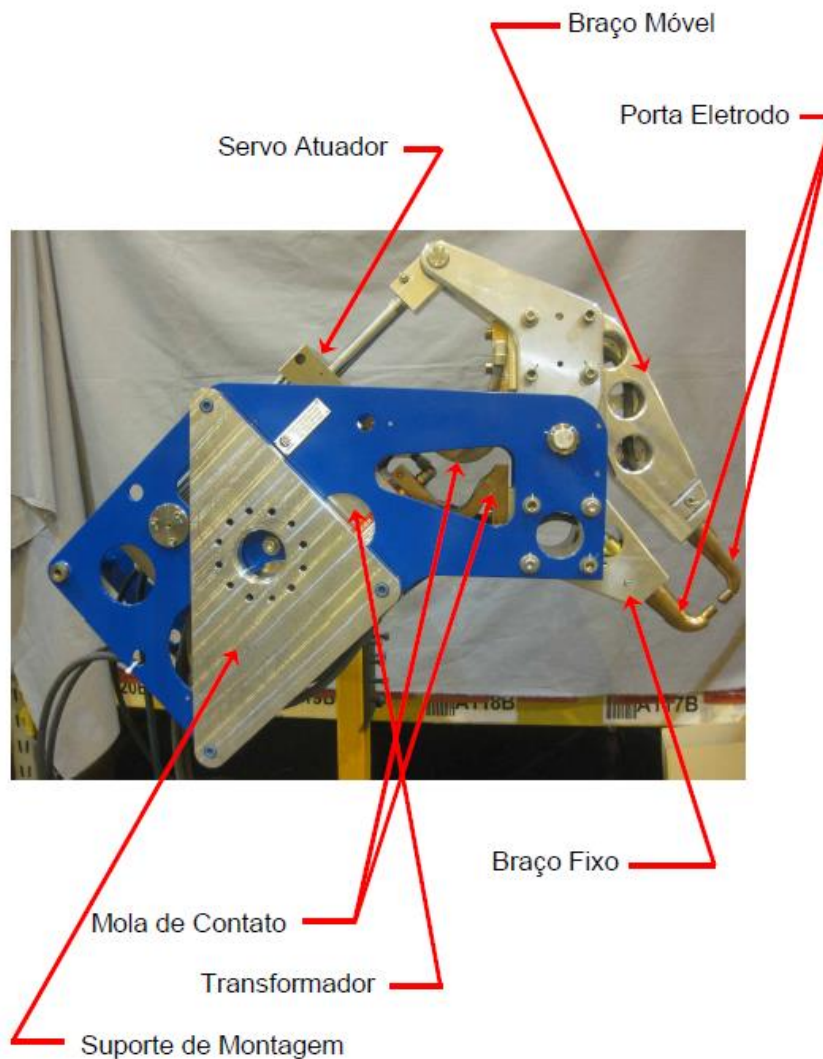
Componentes de uma Pinça de Solda Automática
